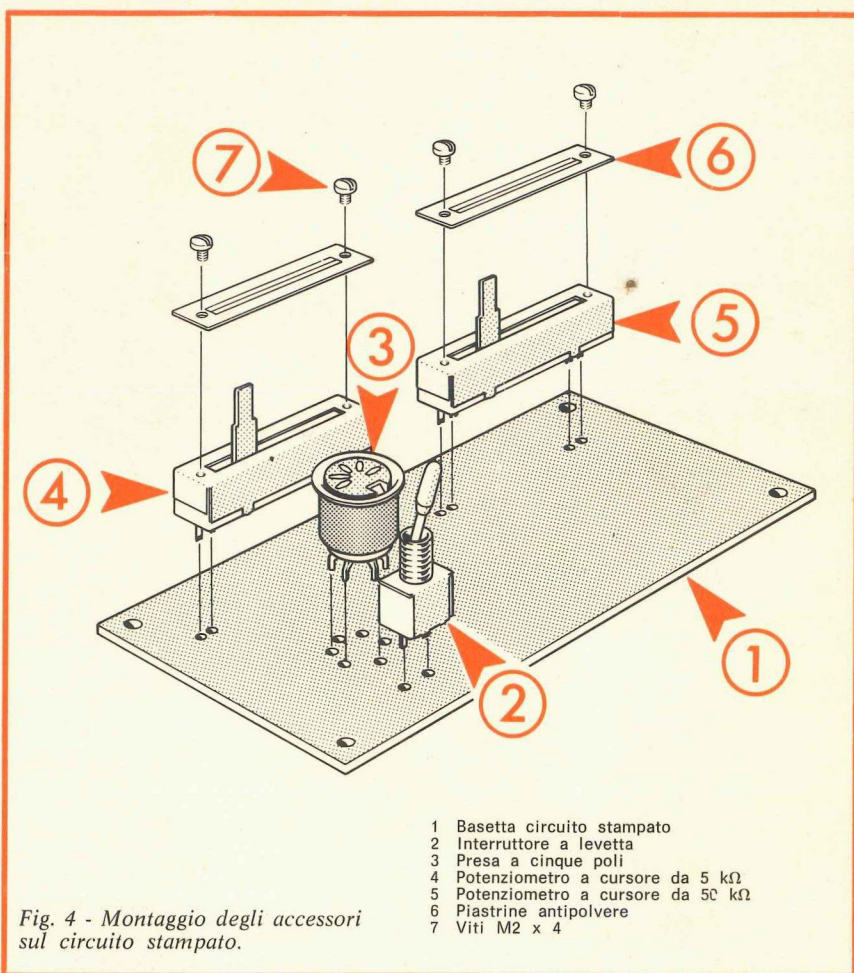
Montaggio degli accessori sul circuito stampato.
